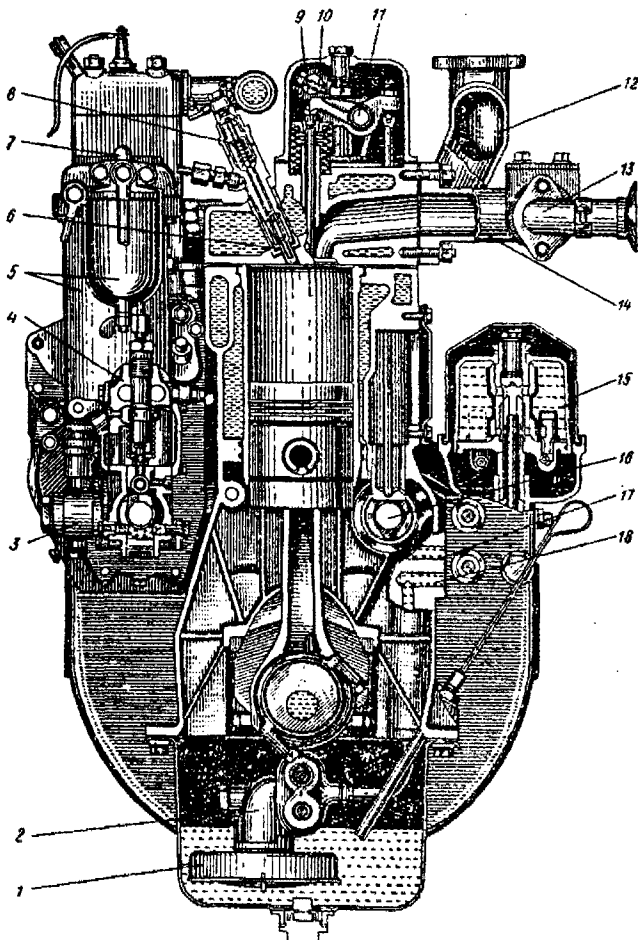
Дизель Д-65Н (поперечный разрез): 1 – заборник масла; 2 – масляный насос; 3 – подкачивающий насос; 4 – топливный насос; 5 – топливные фильтры; 6 – стакан форсунок; 7 – пусковой двигатель; 8 – форсунка; 9 – коромысло клапана; 10 – механизм декомпрессии; 11 – валик коромысла; 12 – выпускной коллектор; 13 – патрубок выпуска газов пускового двигателя; 14 – впускной коллектор; 15 – масляный фильтр; 16 – распределительный вал; 17 – канал подвода масла в магистраль; 18 – канал подвода масла от насоса в фильтр
